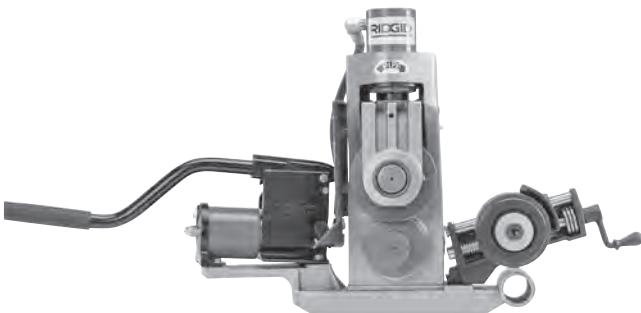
B – Montaje de la ranuradora 918 sobre la base del accionamiento motorizado 300
